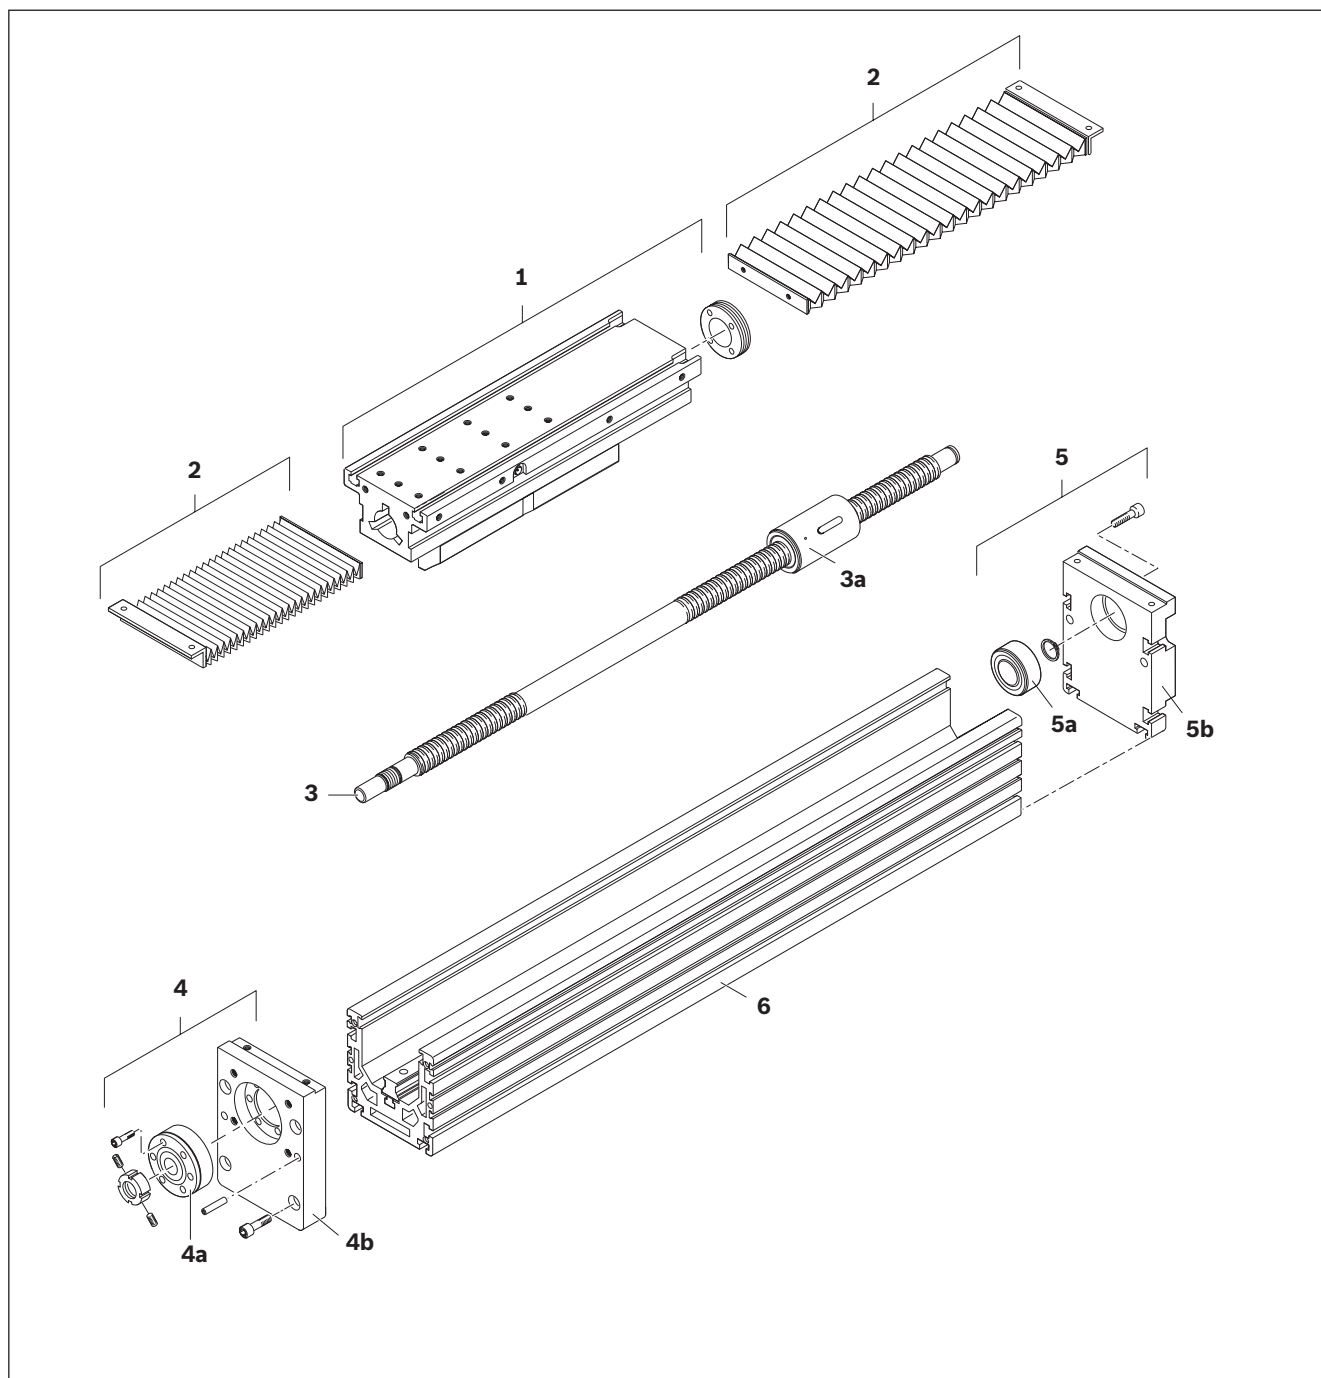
Vue d'ensemble MKK-165-NN-2
